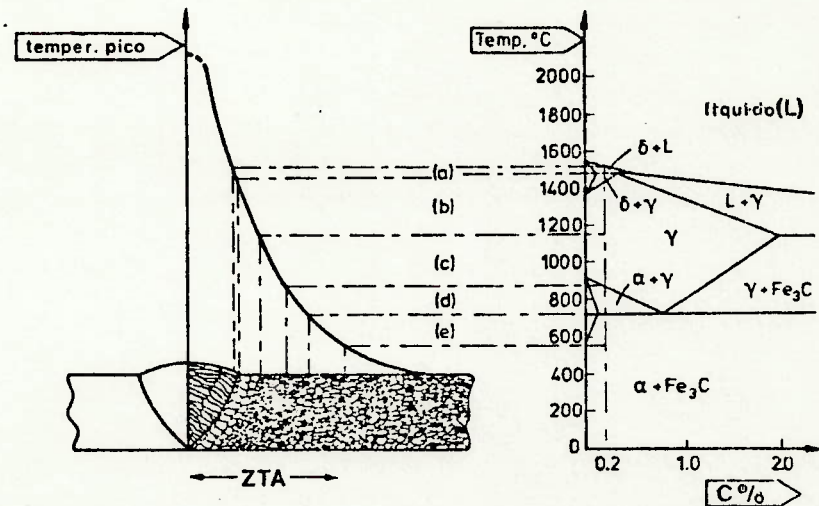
Microestruturas formadas na soldagem, por um único passe 'e'.
